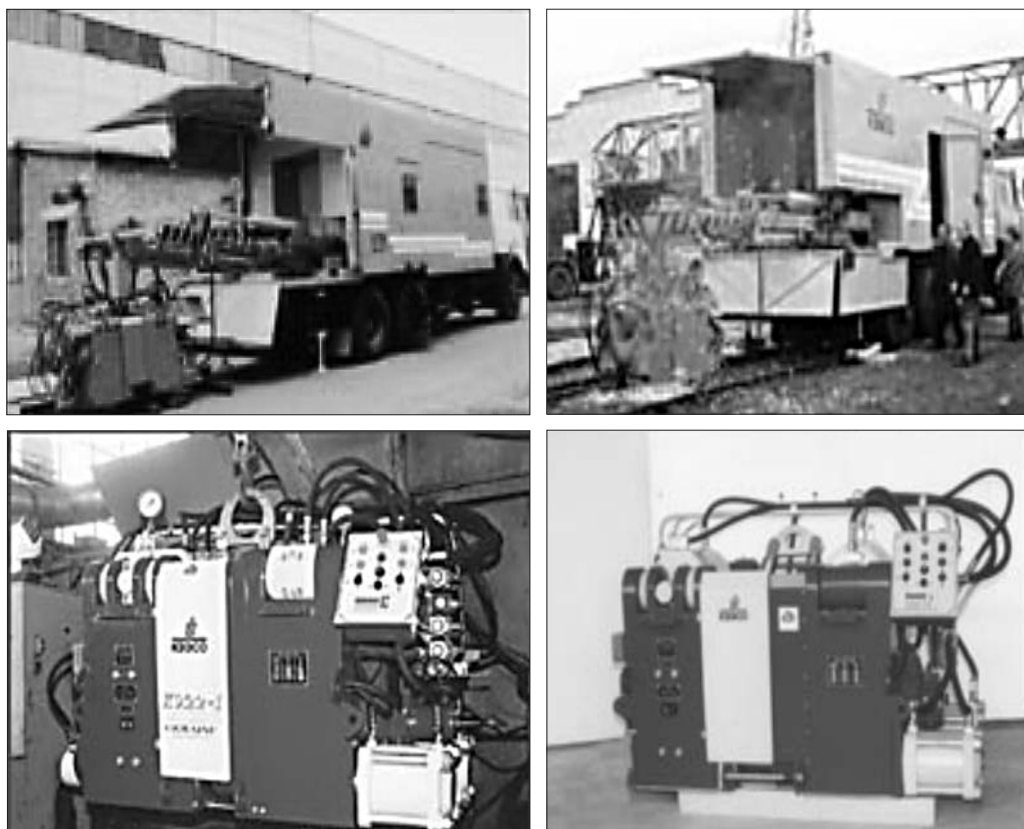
Современные машины для контактной сварки высокопрочных железнодорожных рельсов
